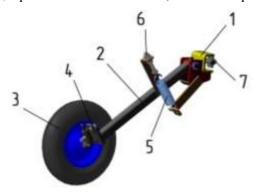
Колесо прикатывающее 1 — кронштейн; 2 — балка; 3 — колесо; 4 —упор; 5 — пружина; 6 — натяжник; 7 — болт.
